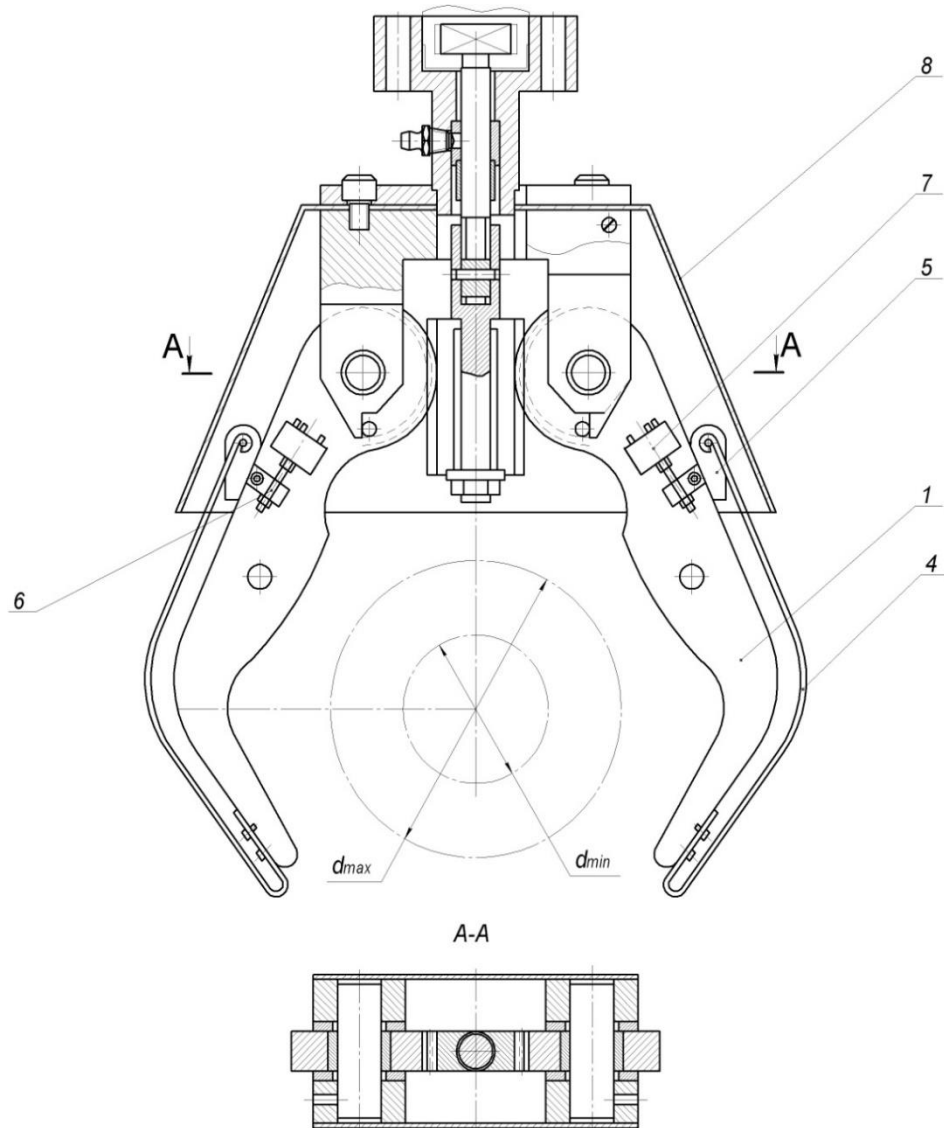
Захватний пристрій для утримання гладкого валу
